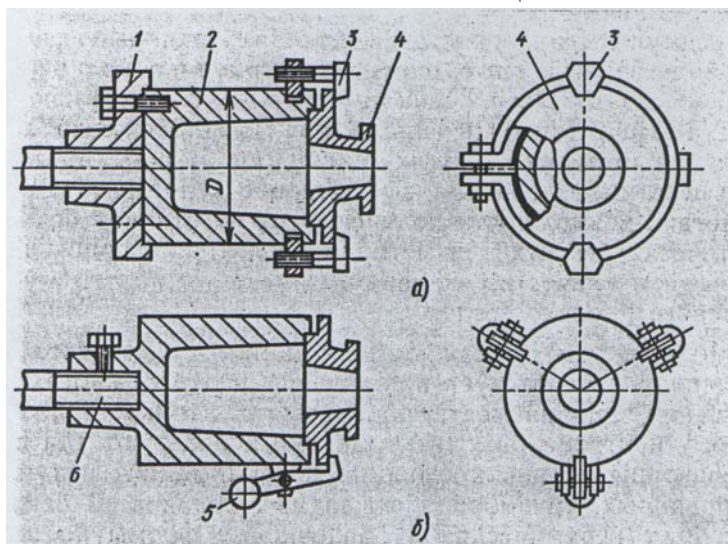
Способы крепления крышек на изложницах. 1- планшайба, 2- форма, 3- болт, 4- крышка, 5- центробежный зажим, 6 - шпindelъ.
